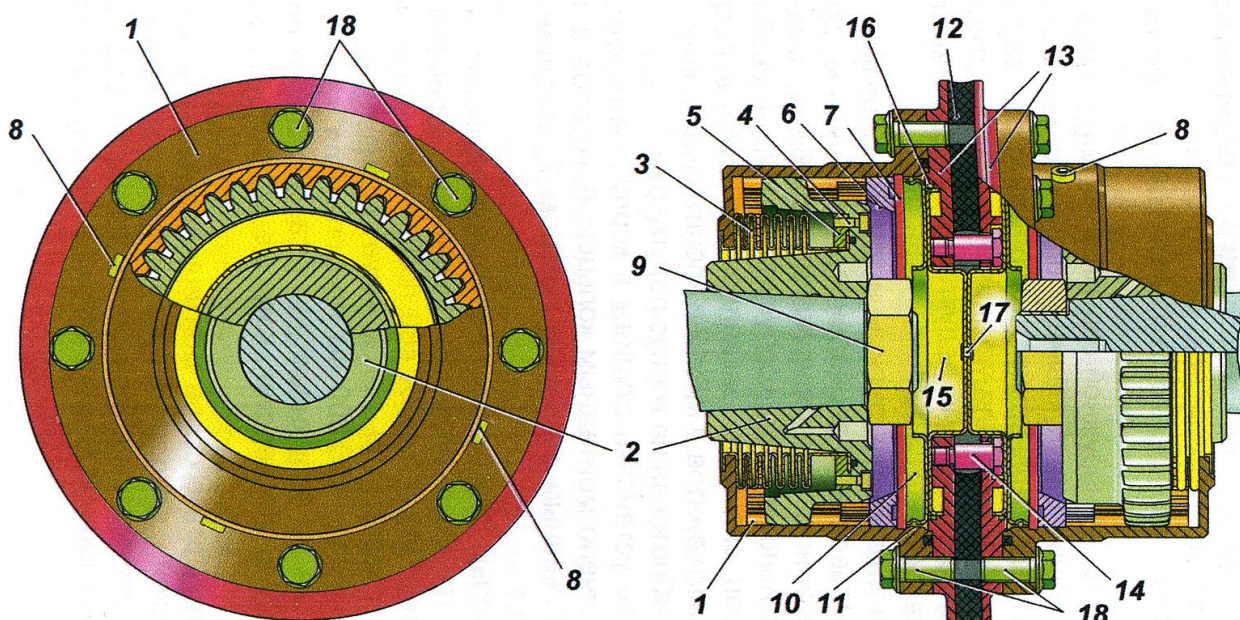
Устройство зубчатой муфты ZK 163-3-BD-HE
